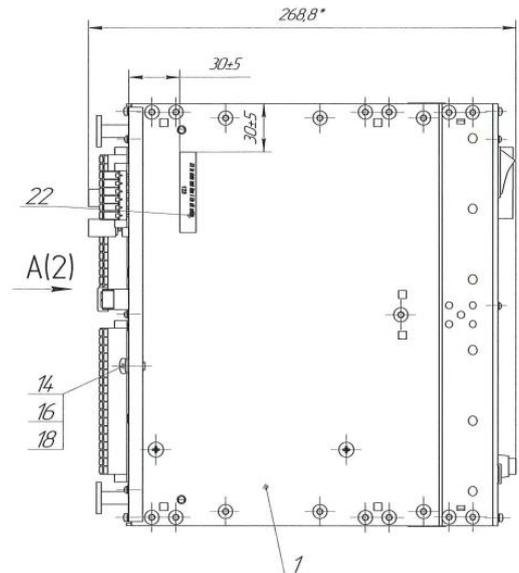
Габаритные и установочные размеры ЭКРА 253 0201 (вид сбоку)
